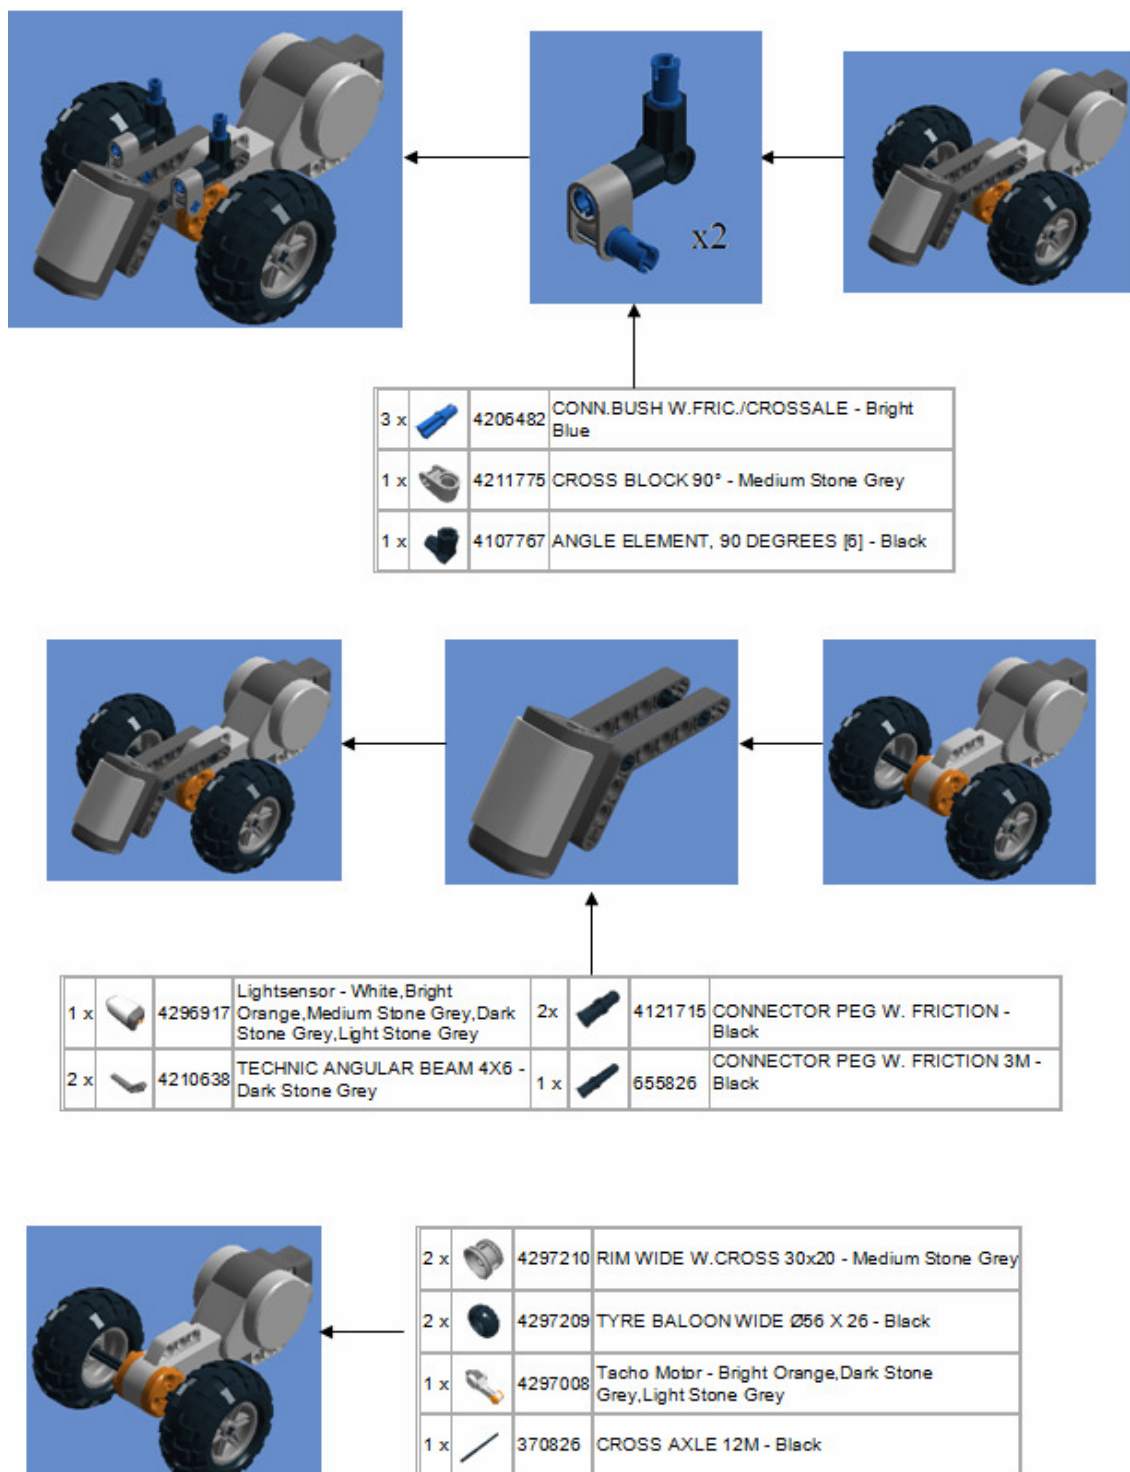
B.B2.2): Montaje de la Segunda parte, apoyo delantero.
